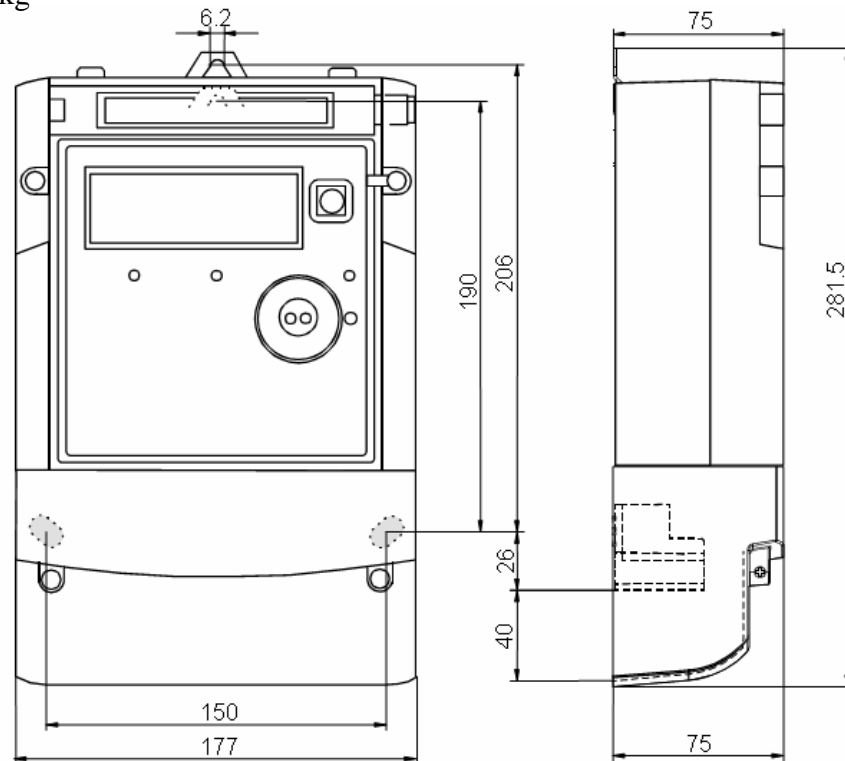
Dimensões do contador Z.G300CR / Z.G400CR
